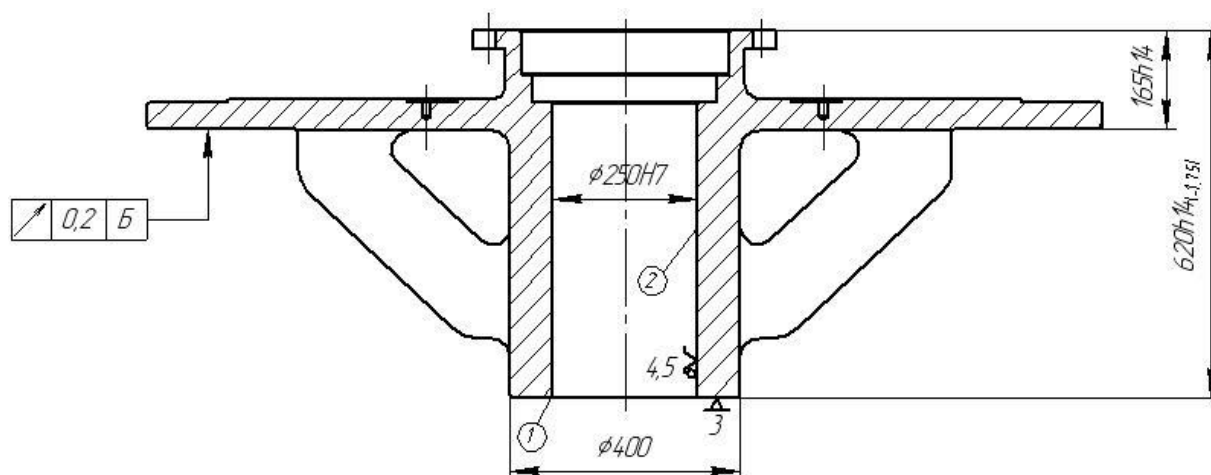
Схема базування деталі при контролі торцевого биття
